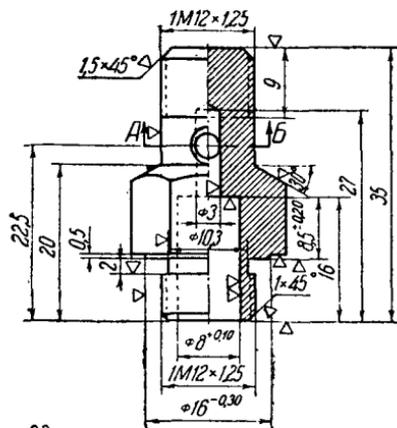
№ 16-01. Корпус фильтра поплавковой камеры для керосина
